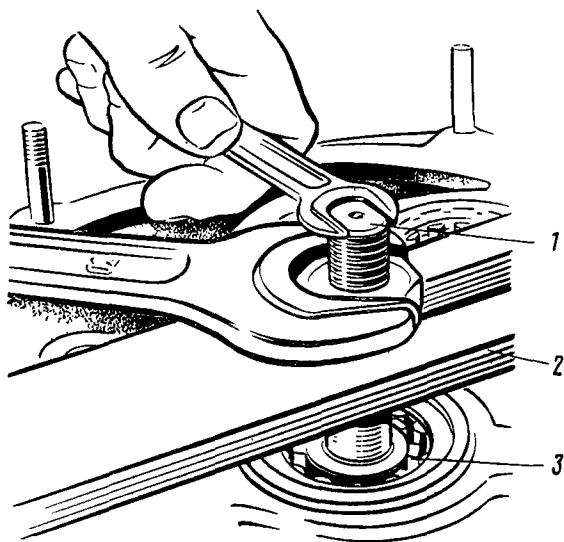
Выпрессовка роликового подшипника шестерни-вала главной передачи:
